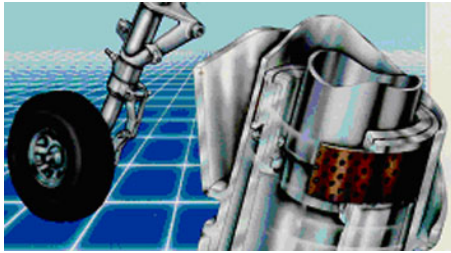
erZ) Cu-Sn-Lager in Radaufhängung eines Flugzeuges
